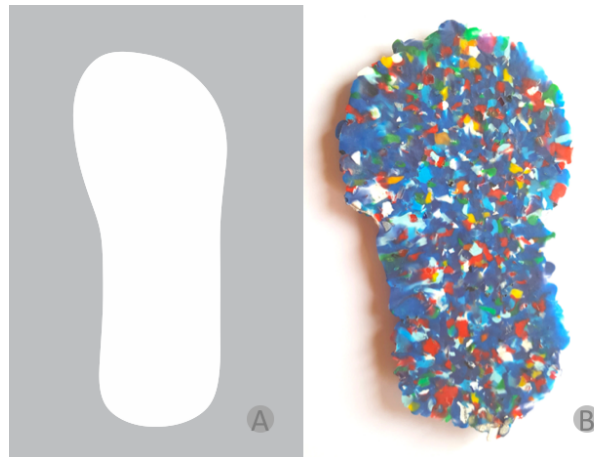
Exp.1: A) Molde de madeira (270x190x10 mm), B) Mix PE.
